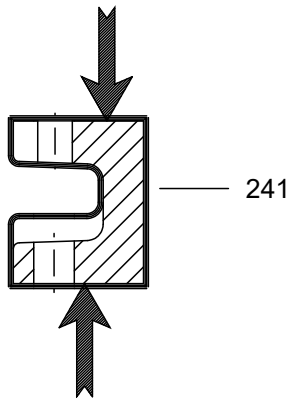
Emplacements d'inspection de la surface du pied de cadre
